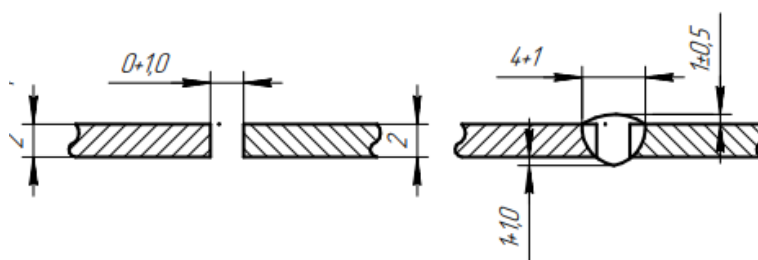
Подготовка кромок и форма шва сварного соединения
